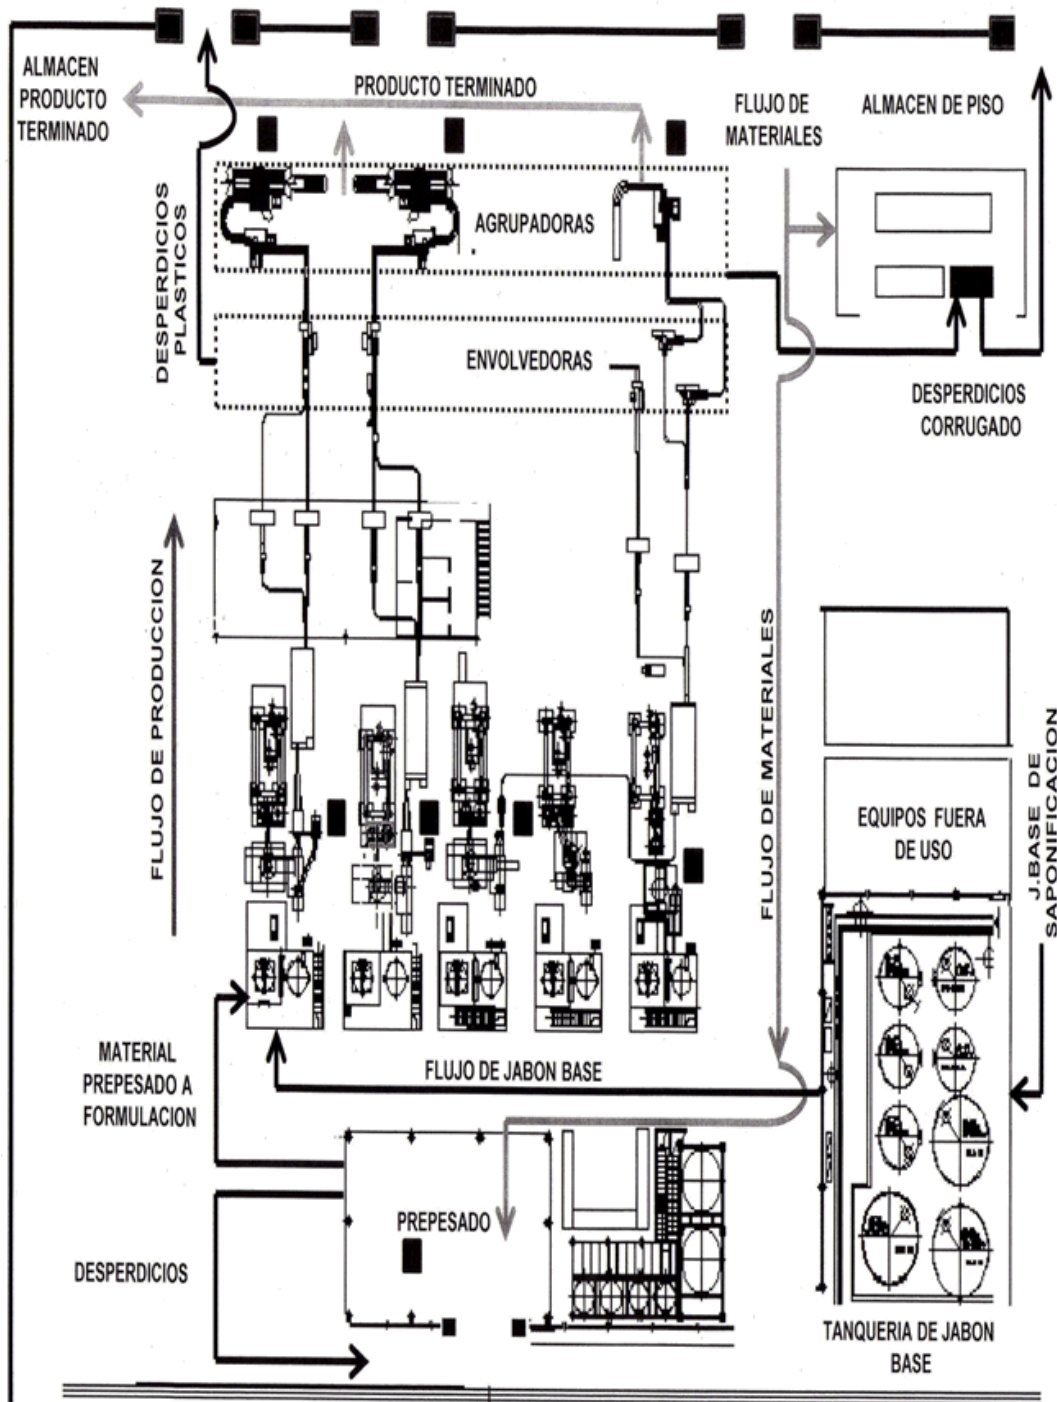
Layout del área de jabonería de Planta Limpieza (Valencia)
